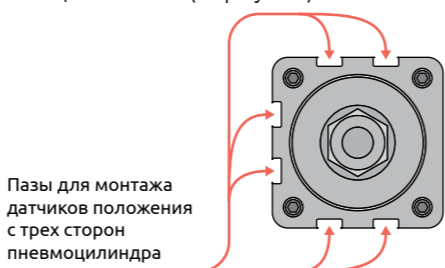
Расположение пазов на корпусе пневмоцилиндра для монтажа датчиков положения
